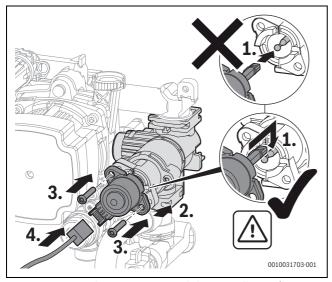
Remonter le moteur au niveau de la vanne sélective (variante avec vis)
